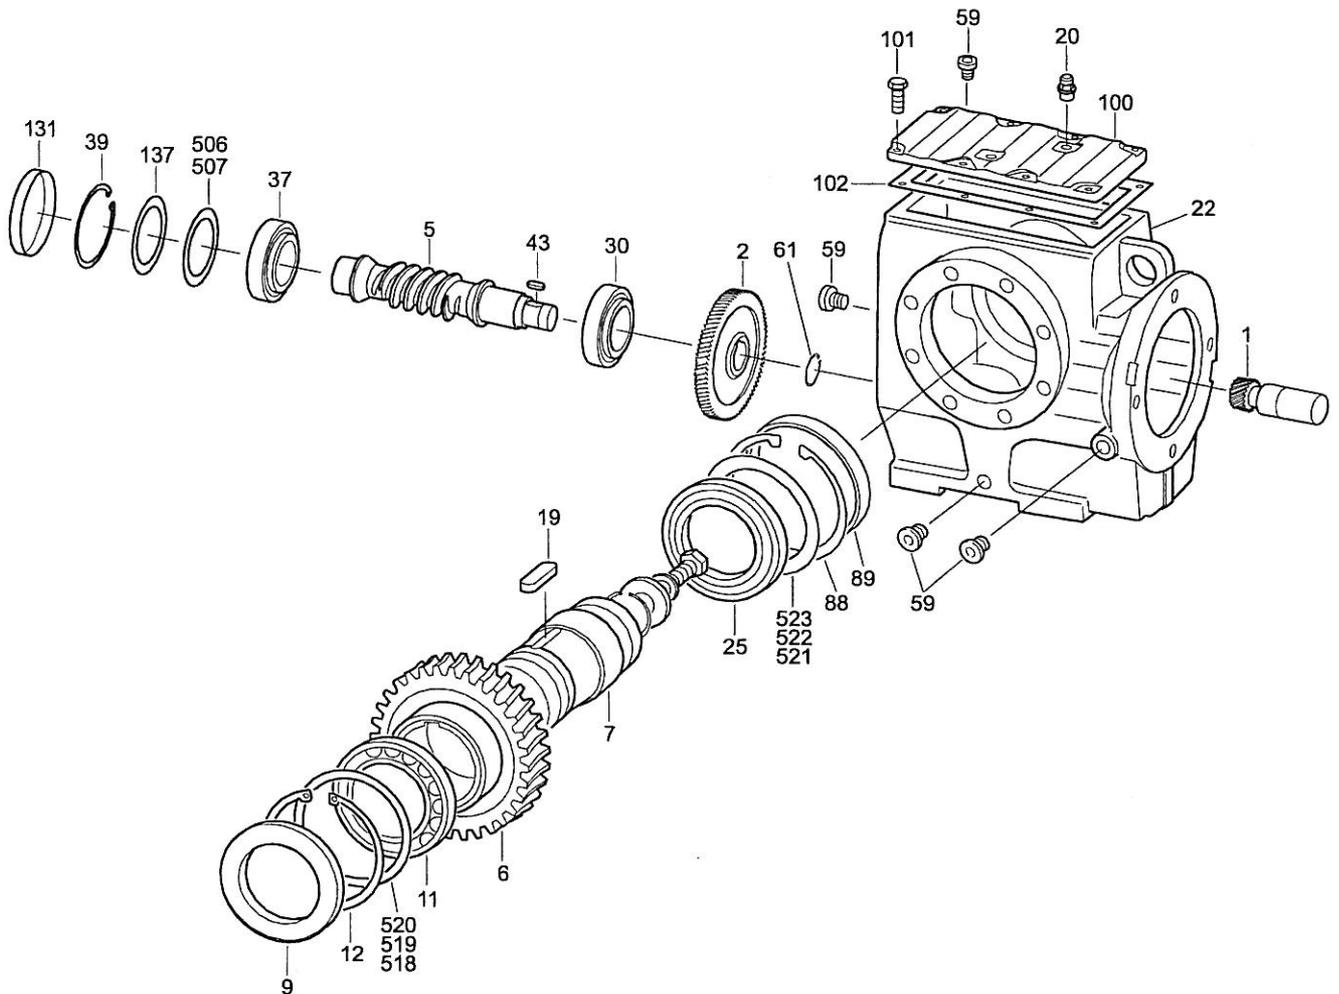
Prinzipieller Aufbau Schneckengetriebe
